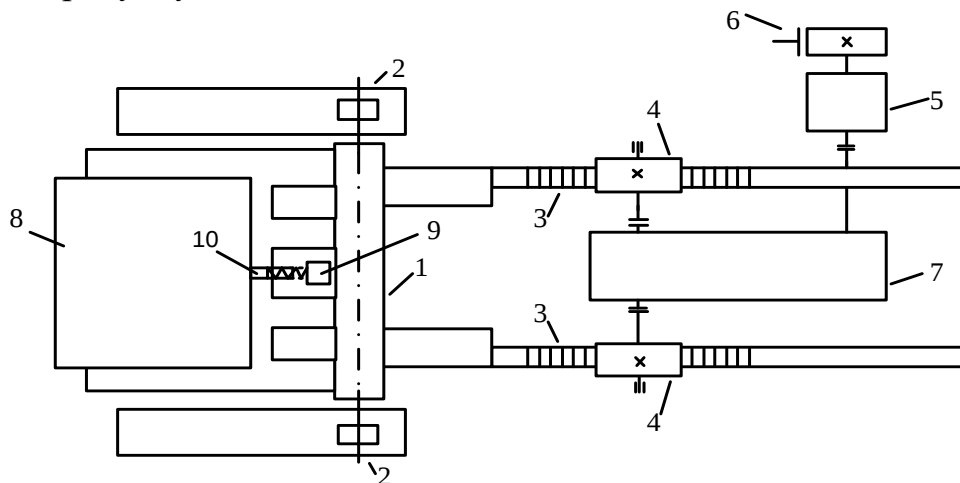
Кінематична схема зіштовхувача: 1- штовхач, 2 - опорні ролики, 3 - зубчаста рейка, 4 - ведуче колесо, 5 - двигун, 6 - гальмо, 7 - редуктор, 8 - заготовка, 9 - кінцевий вимикач, 10 - підпружинений шток кінцевого вимикача
